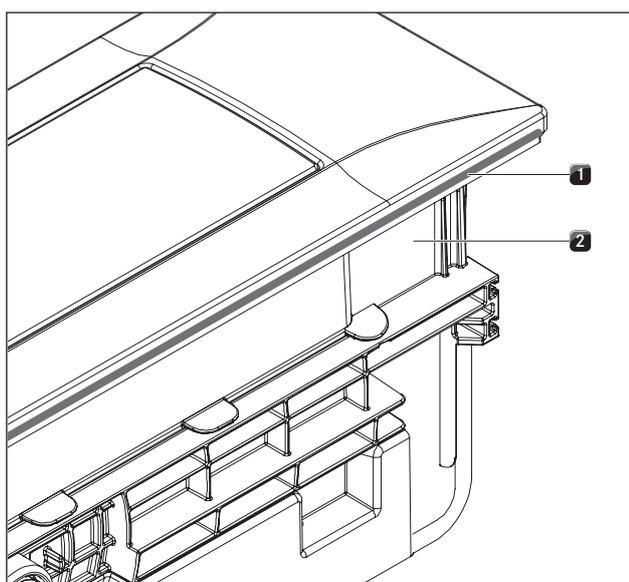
Remover o friso de plástico lateral no extrator de superfície
